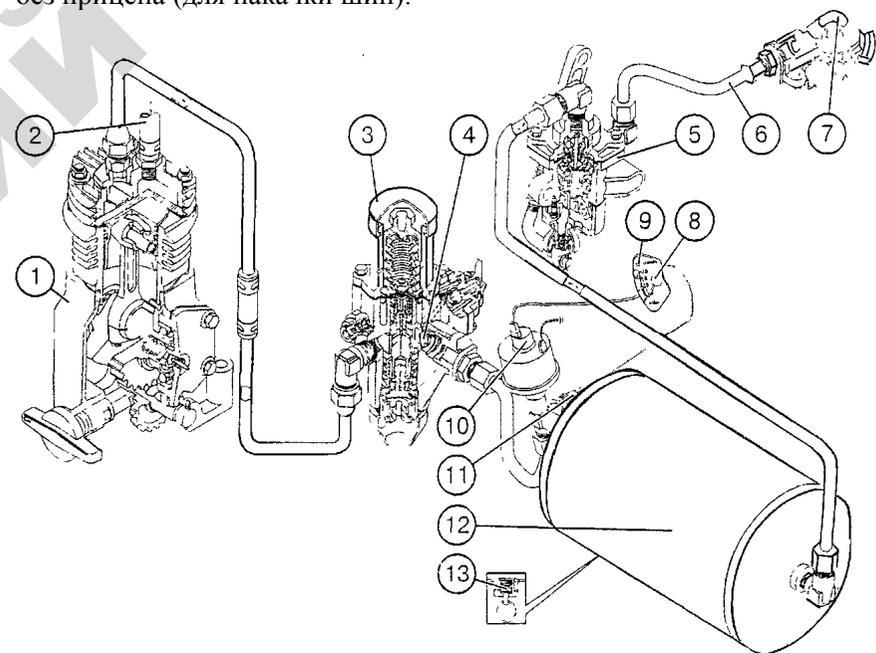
Пневмопривод тормозов прицепа трактора «Беларус-1522»:
